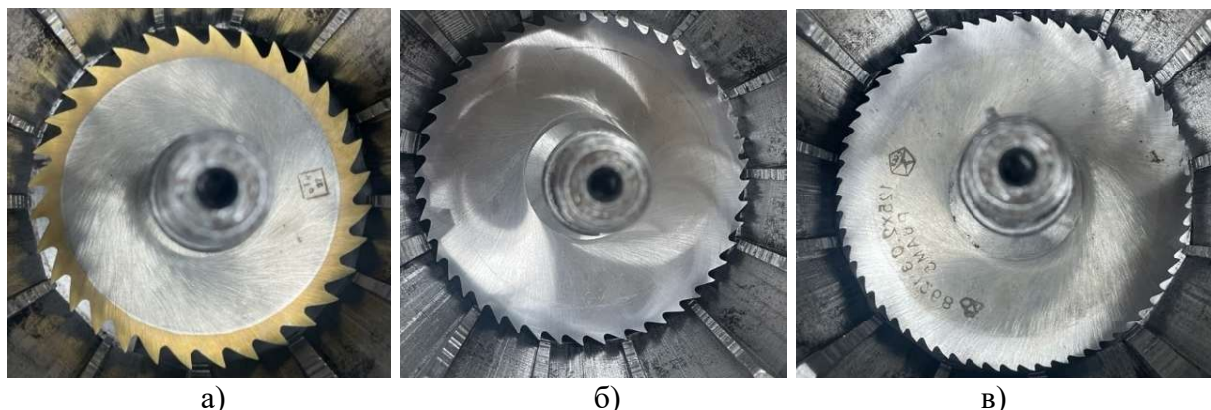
Ножи ротора измельчителя, расположенные в статоре:
